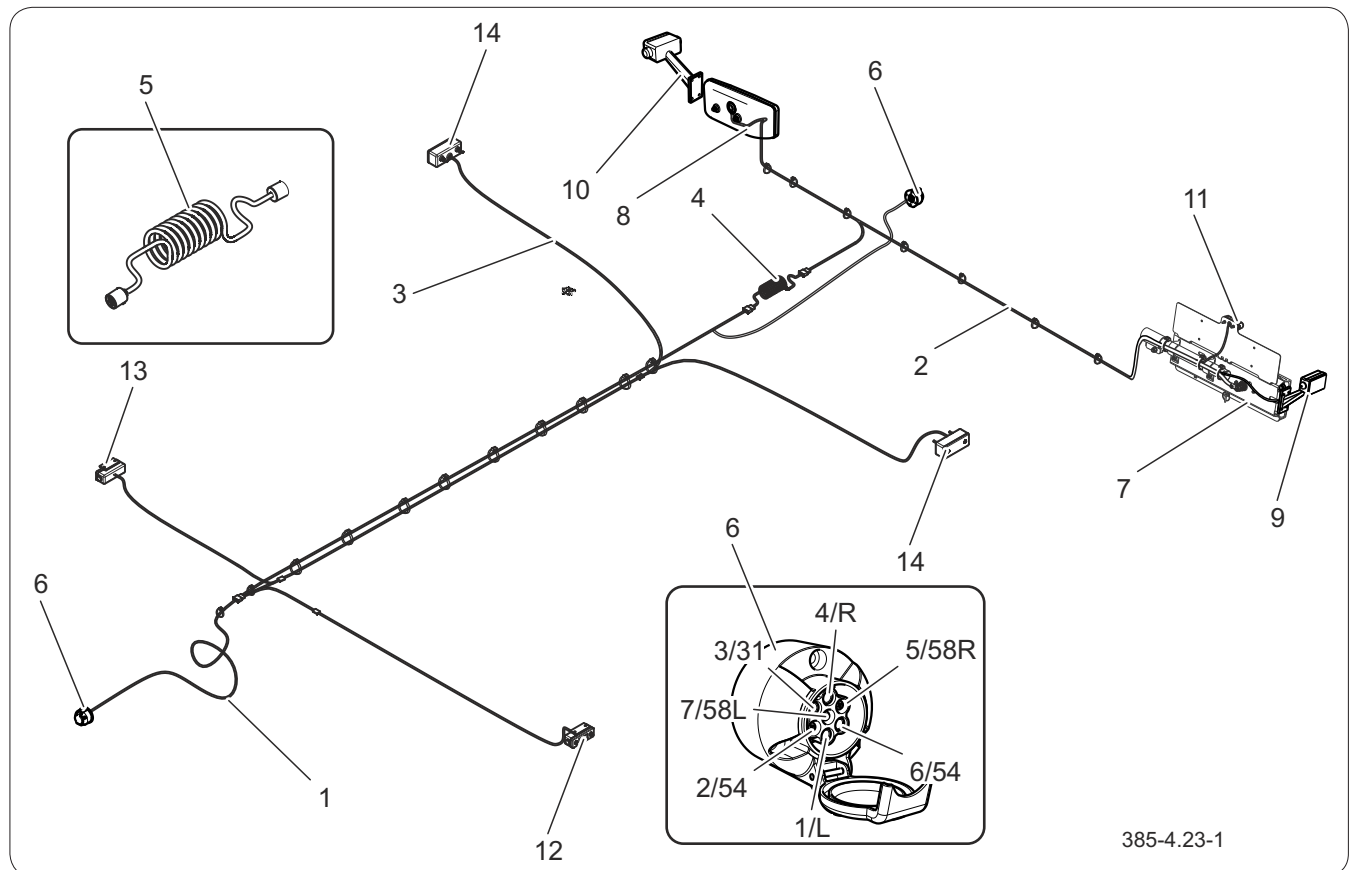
Budowa i schemat instalacji elektrycznej układu hydraulicznego
